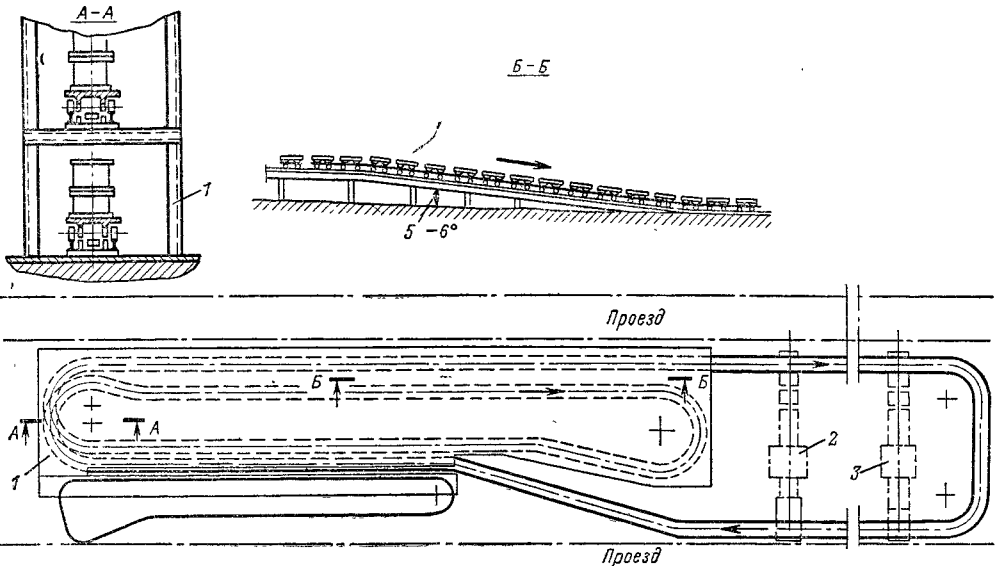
Пространственный горизонтально-замкнутый тележечный литейный конвейер: 1 — охладительный кожух; 2 — формовка верхней полуформы; 3 — формовка нижней полуформы
